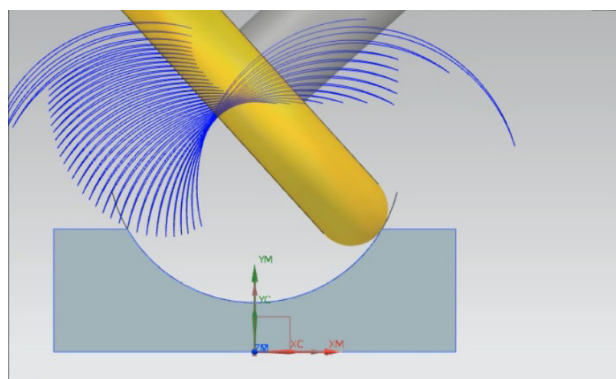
Модель траектории движения инструмента с возвратно-качательным движением подачи
